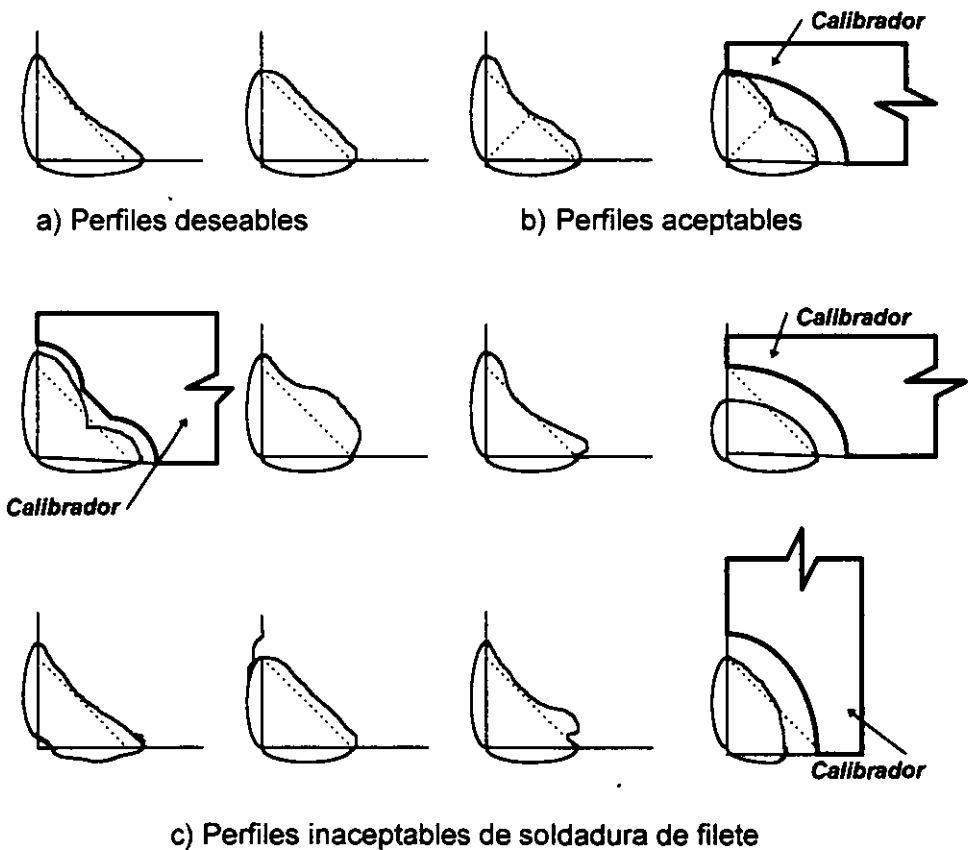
Perfiles de las soldaduras y calibradores
